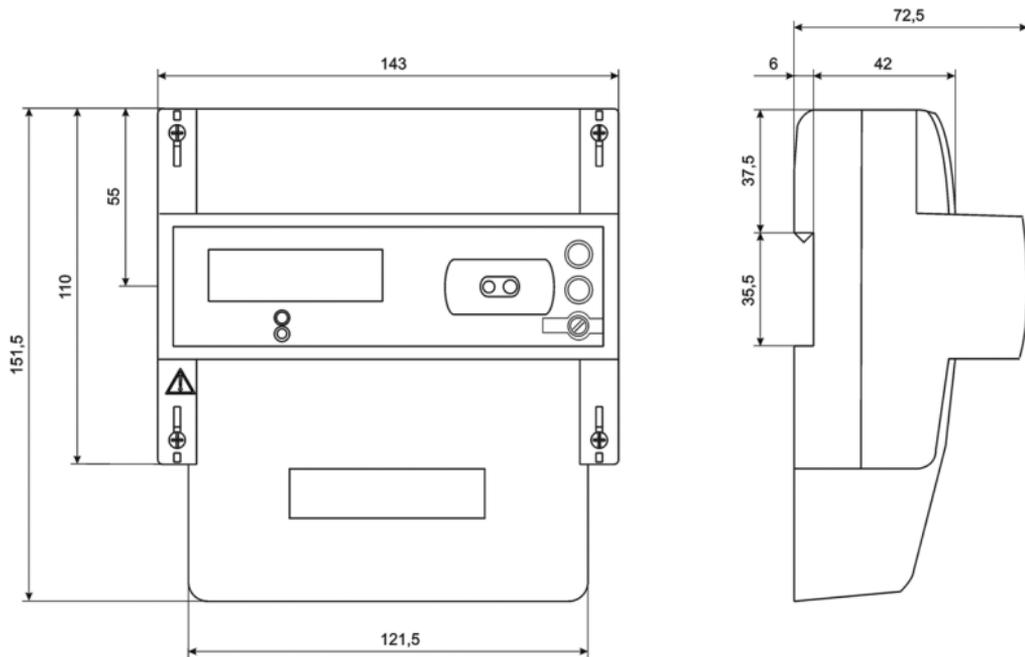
Габаритные и установочные размеры счетчика SE306 S31
